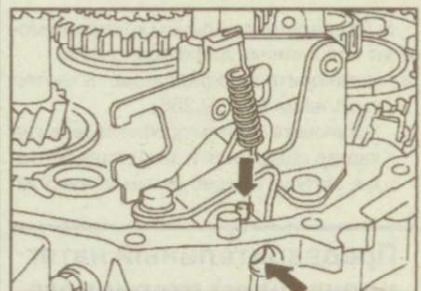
Установка вала рычага передачи заднего хода и штифта
